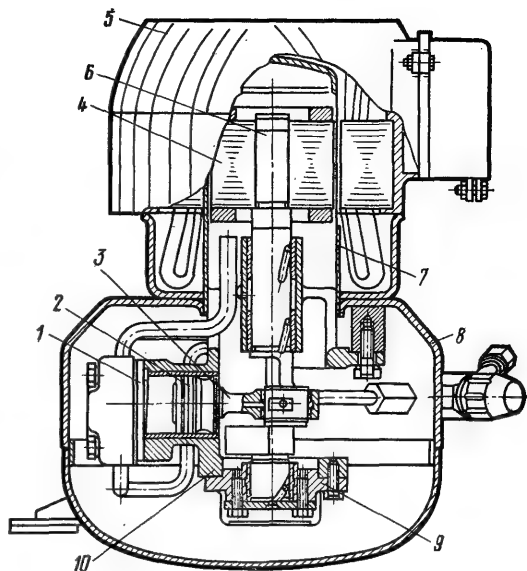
Конструкция экранированных компрессоров ФГЭС 0,7~3 (2) и ФГЭС 1,1~3 (2): 1 — клапанная группа; 2 — поршень; 3 — шатун; 4 — ротор; 5 — статор; 6 — эксцентриковый вал; 7 — экран; 8 — кожух; 9 — опора вала; 10 — корпус.
